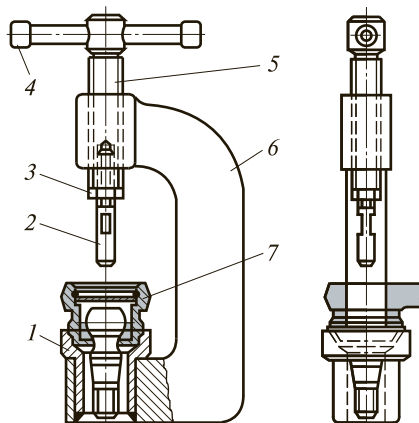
Приспособление для сборки шарниров рулевых тяг:
